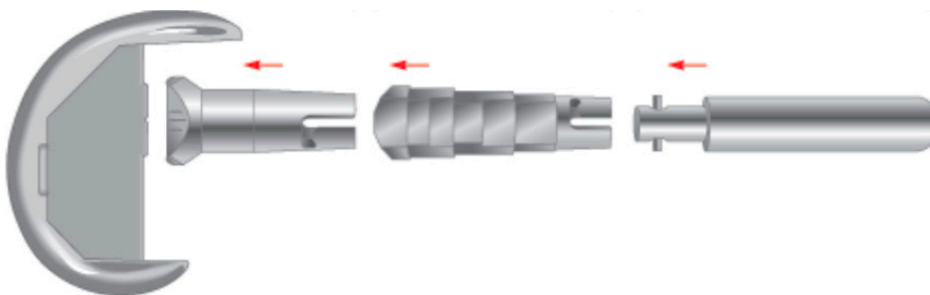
Montaje del componente femoral. Tomada de técnica quirúrgica
